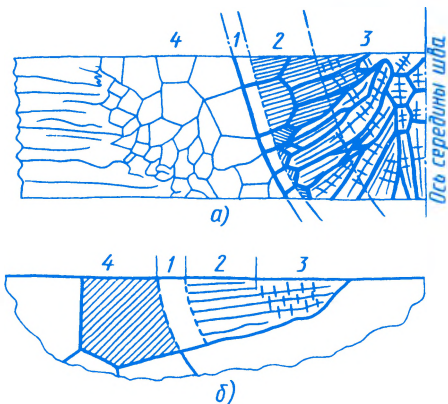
Типы кристаллической структуры сварного металла:
